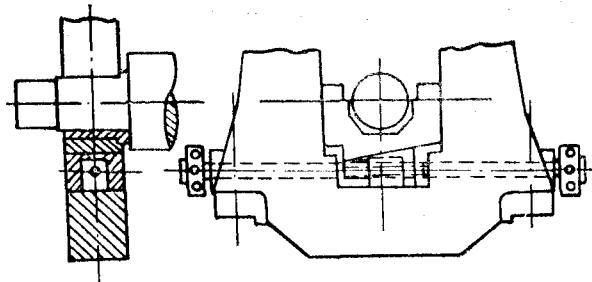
Схема установочного механизма нижнего вала с поперечным клином
